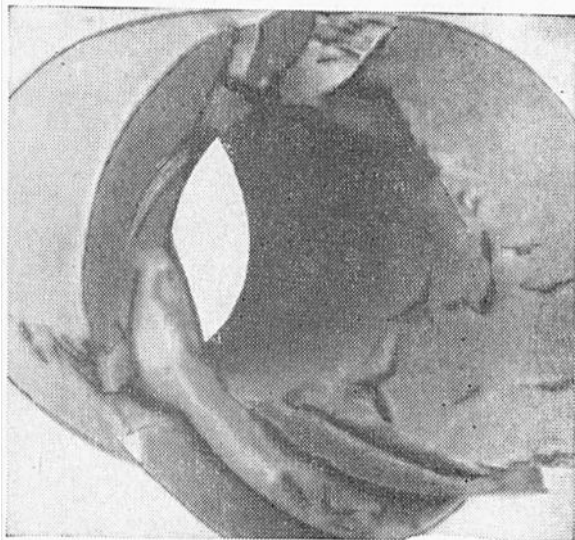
Разрушенная трубная заготовка из высоколегированной стали X8CrNiTi18.10.
